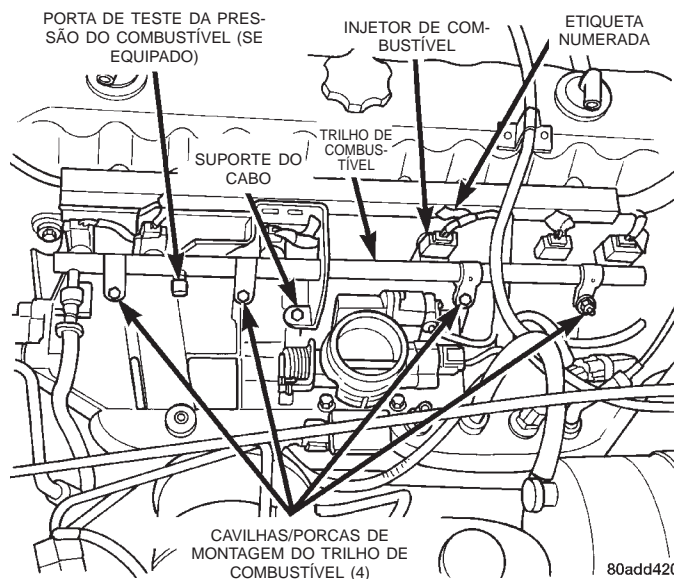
Montagem do Trilho de Combustível—Motor 4.0L
